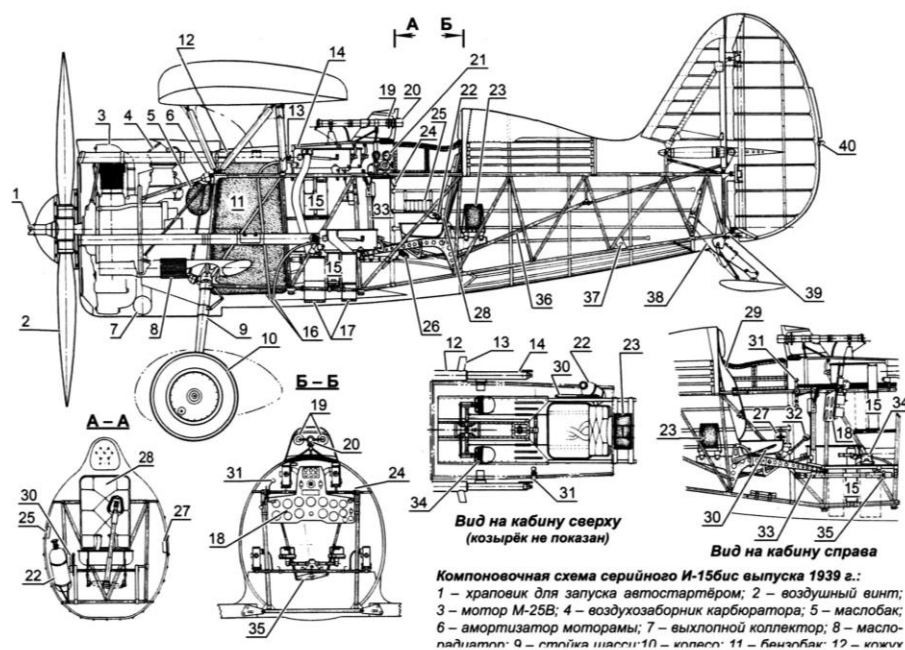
Plano 2. Perfil detallado del I-15bis
